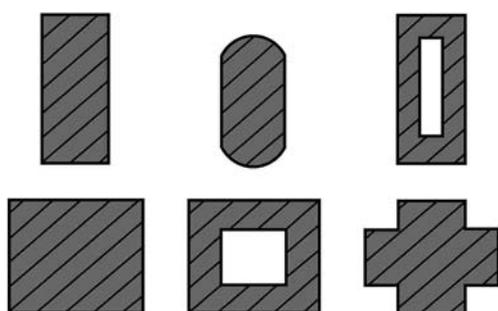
Mögliche Fügequerschnitte für das Orbitalreißschweißen
